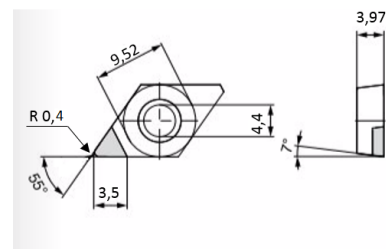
Dimensões em mm da pastilha de corte [60]
